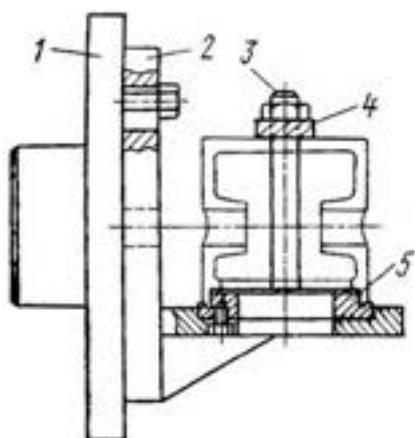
Приспособление для обработки отверстия под поршневой палец:
